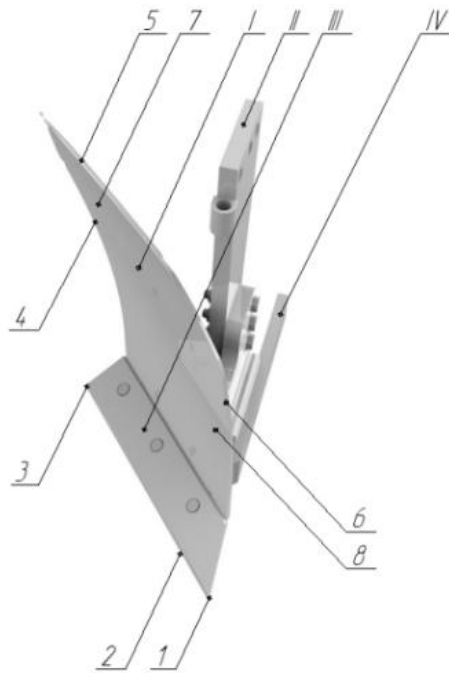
Лемішно - відвальний плужний корпус:
